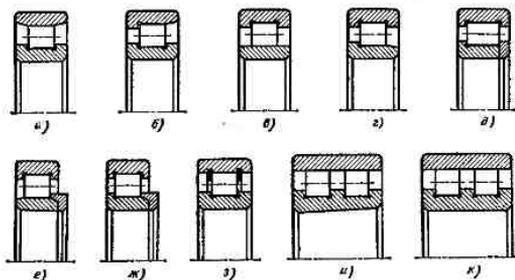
Роликподшипники с короткими цилиндрическими роликами типов: а - 2000; б - 12600; в - 32000; г - 42000; д - 62600; е - 62000; ж - 62000; з - 102000; и - 3182000; к - 3282000
